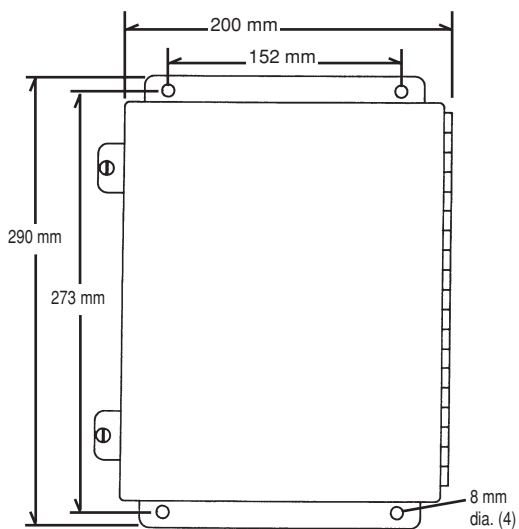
Dimensioni di montaggio– Rilevamento di altezza iniziale
